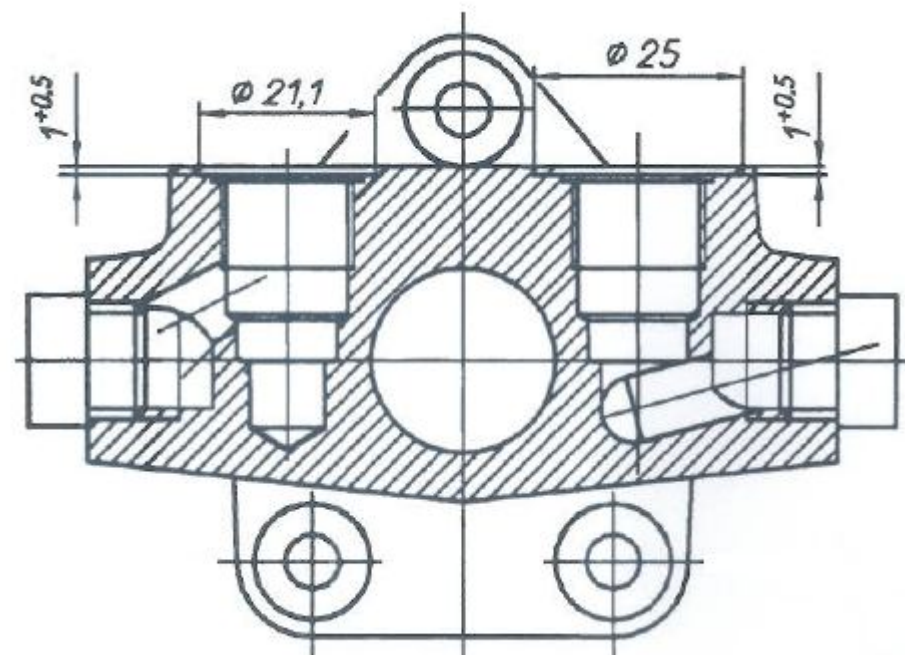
Корпус топливоподкачивающего насоса 236-1106216-Г
